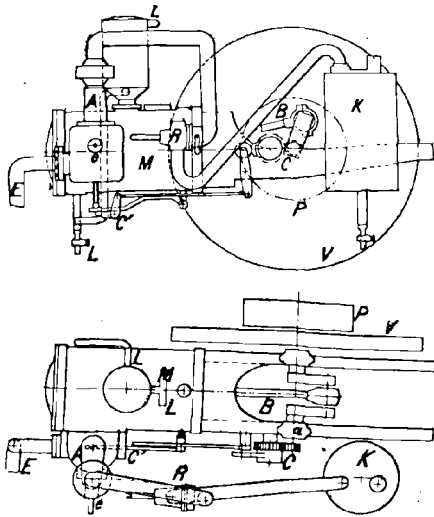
Moteur Benz-Roger monocylindrique horizontal.
